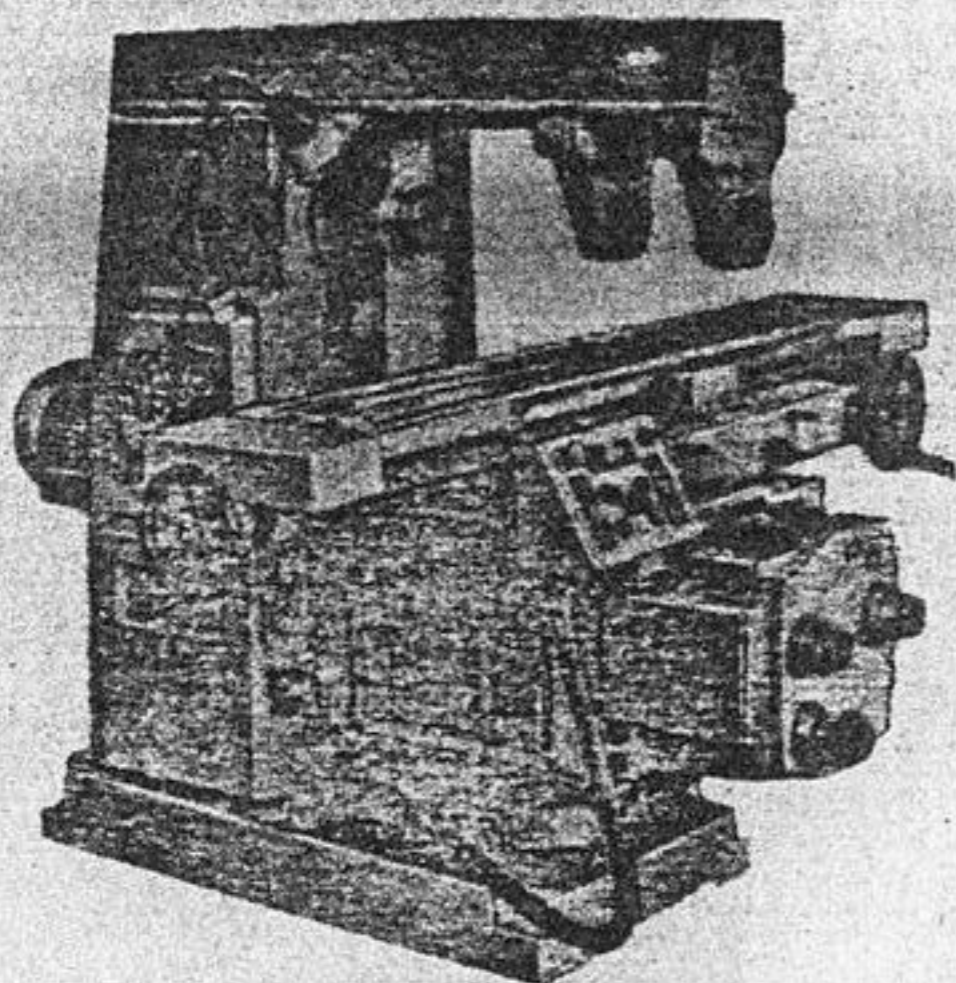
Универсальный консольно-фрезерный станок 6Т83-29
